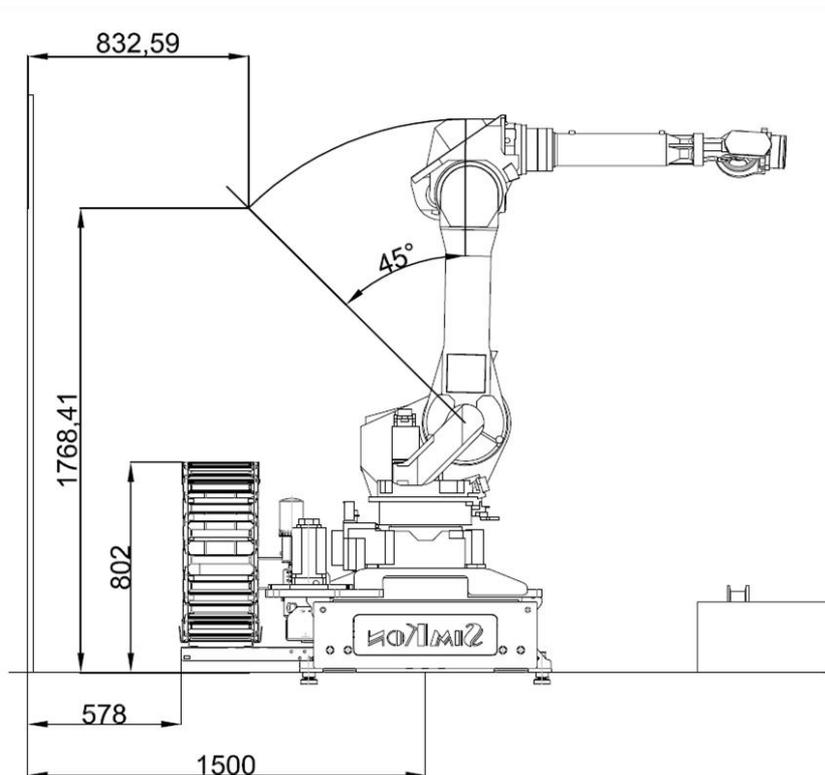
Plano alzado estación detección: distancia a cerramiento
